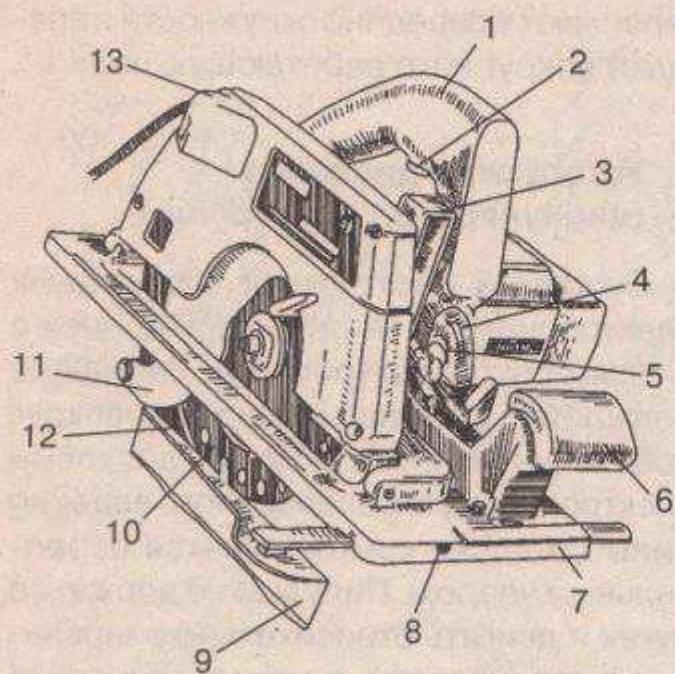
Дисковая (циркулярная) пила PKS 66 фирмы «Bosch»: 1 — ручка; 2 — кнопка-курок; 3 — шкала глубины пропила; 4 — зажим-фиксатор и шкала угла наклона; 5 — зажим-фиксатор глубины пропила; 6 — вспомогательная рукоятка; 7 — лыжа; 8 — визир пропила; 9 — боковая линейка; 10 — полотно; 11 — поворотное ограждение полотна; 12 — расклинивающий нож; 13 — патрубок удаления опилок и пыли
